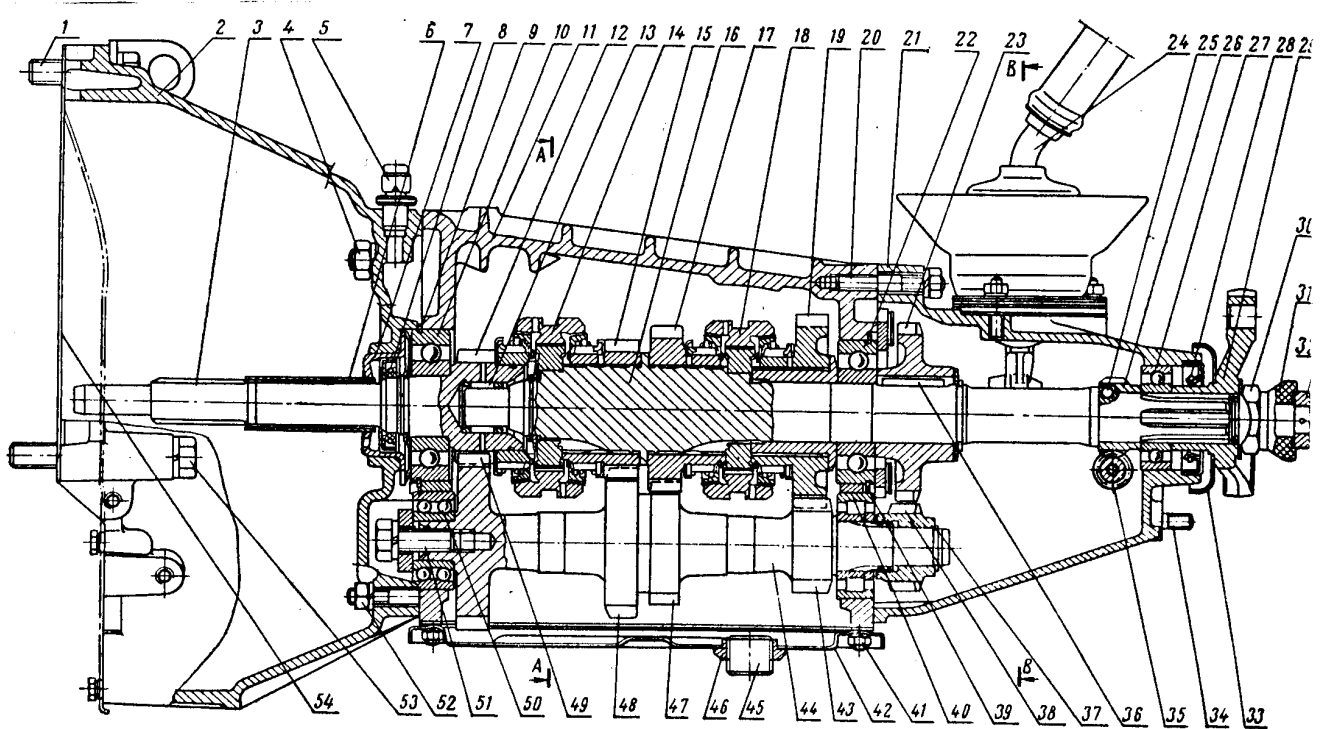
Коробка передач автомобиля ВАЗ-2105.
